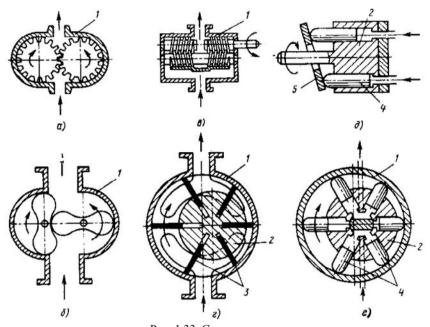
Схемы насосов: а — шестеренный; б — коловратный; в — винтовой; г — шиберный: д — аксиально-поршневой; в — радиально-поршневой; 1 — корпус; 2 — ротор; 3 — лопасти; 4 — плунжеры; 5 — наклонная шайба
